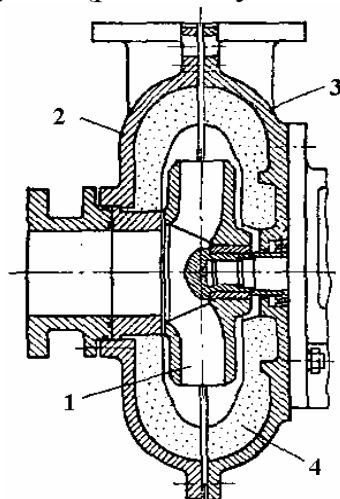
Однокорпусний ґрунтовий насос: 1 – робоче колесо; 2 – передня половина корпусу; 3 – задня половина корпусу; 4 – корундова футеровка
